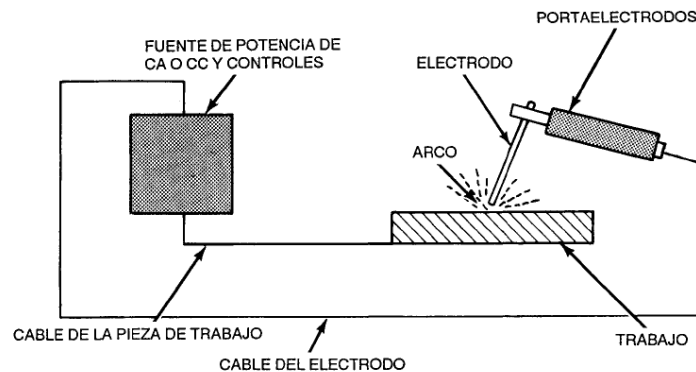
Elementos de un circuito de soldadura típico para soldadura por arco de metal protegido.
